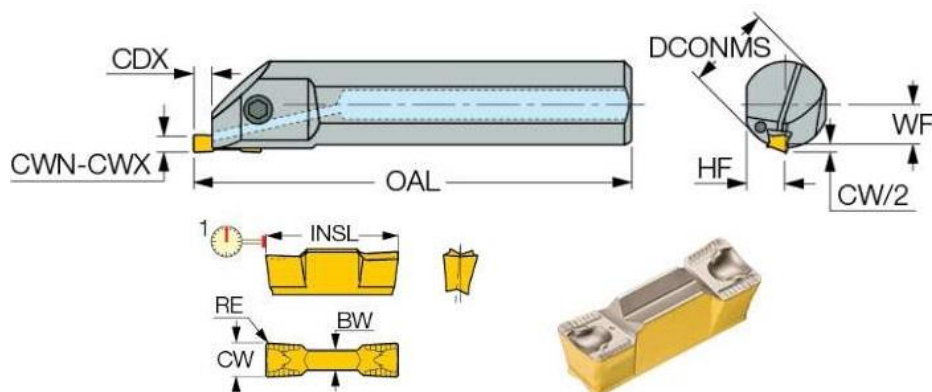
HFIR /L-МС канавочный резец Iscar
